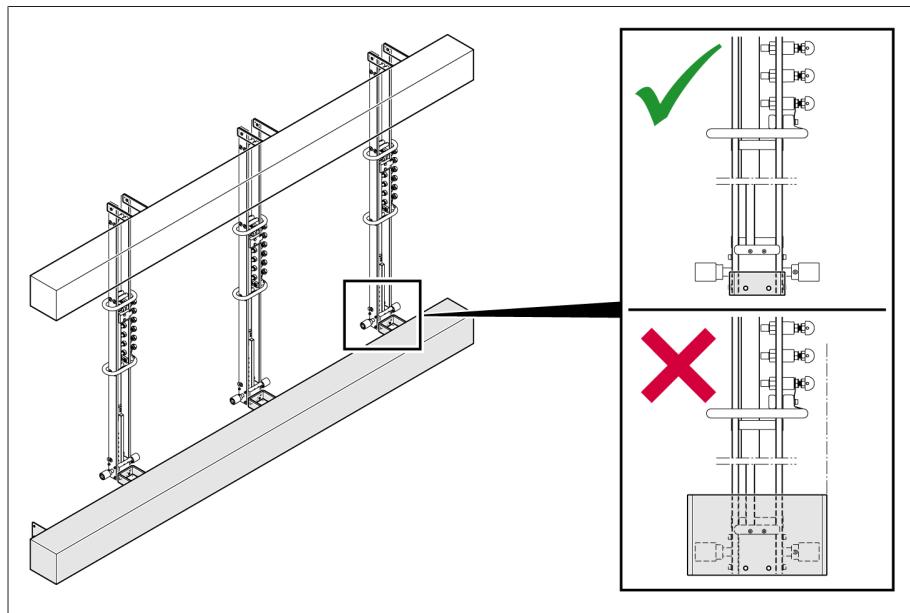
Крепежное приспособление на верхнем редукторе, устройство ПБВ с боковым расположением контактов
